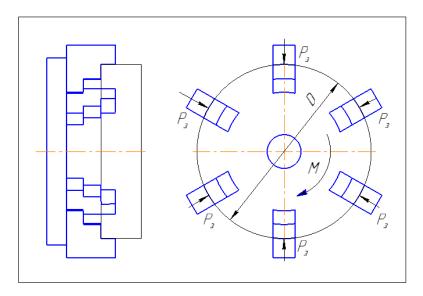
Короткая заготовка в патроне с п кулачками
